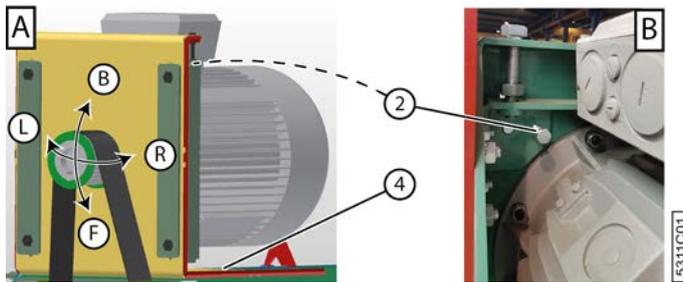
Vue avant [A] et vue arrière détaillée [B] du moteur électrique
